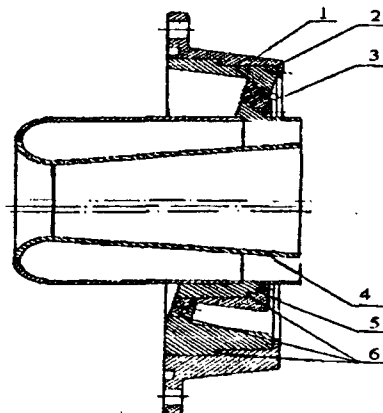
Сопловая крышка, обеспечивающая угловое смещение сопла
